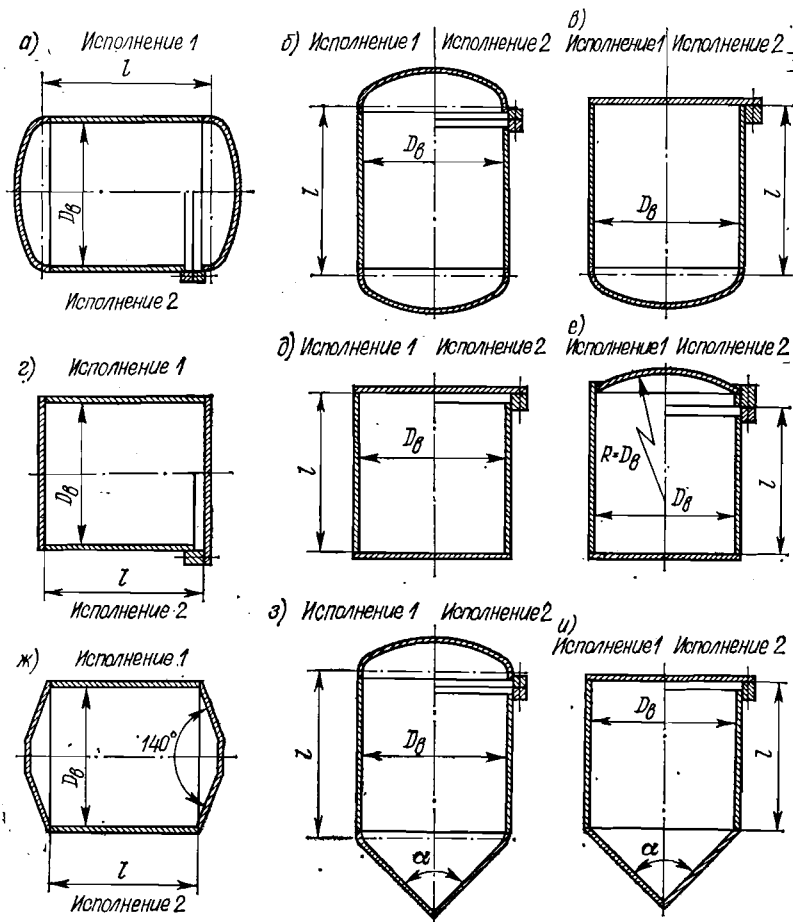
Конструктивные схемы корпусов емкостных стальных сварных цилиндрических аппаратов по ГОСТ 9931—79: а — тип ГЭЭ; б — тип ВЭЭ; в — тип ВЭП; г — тип ГПП; д — тип ВПП; е — тип ВПС; ж — тип ГКК; з — тип ВКЭ; и — тип ВКП
